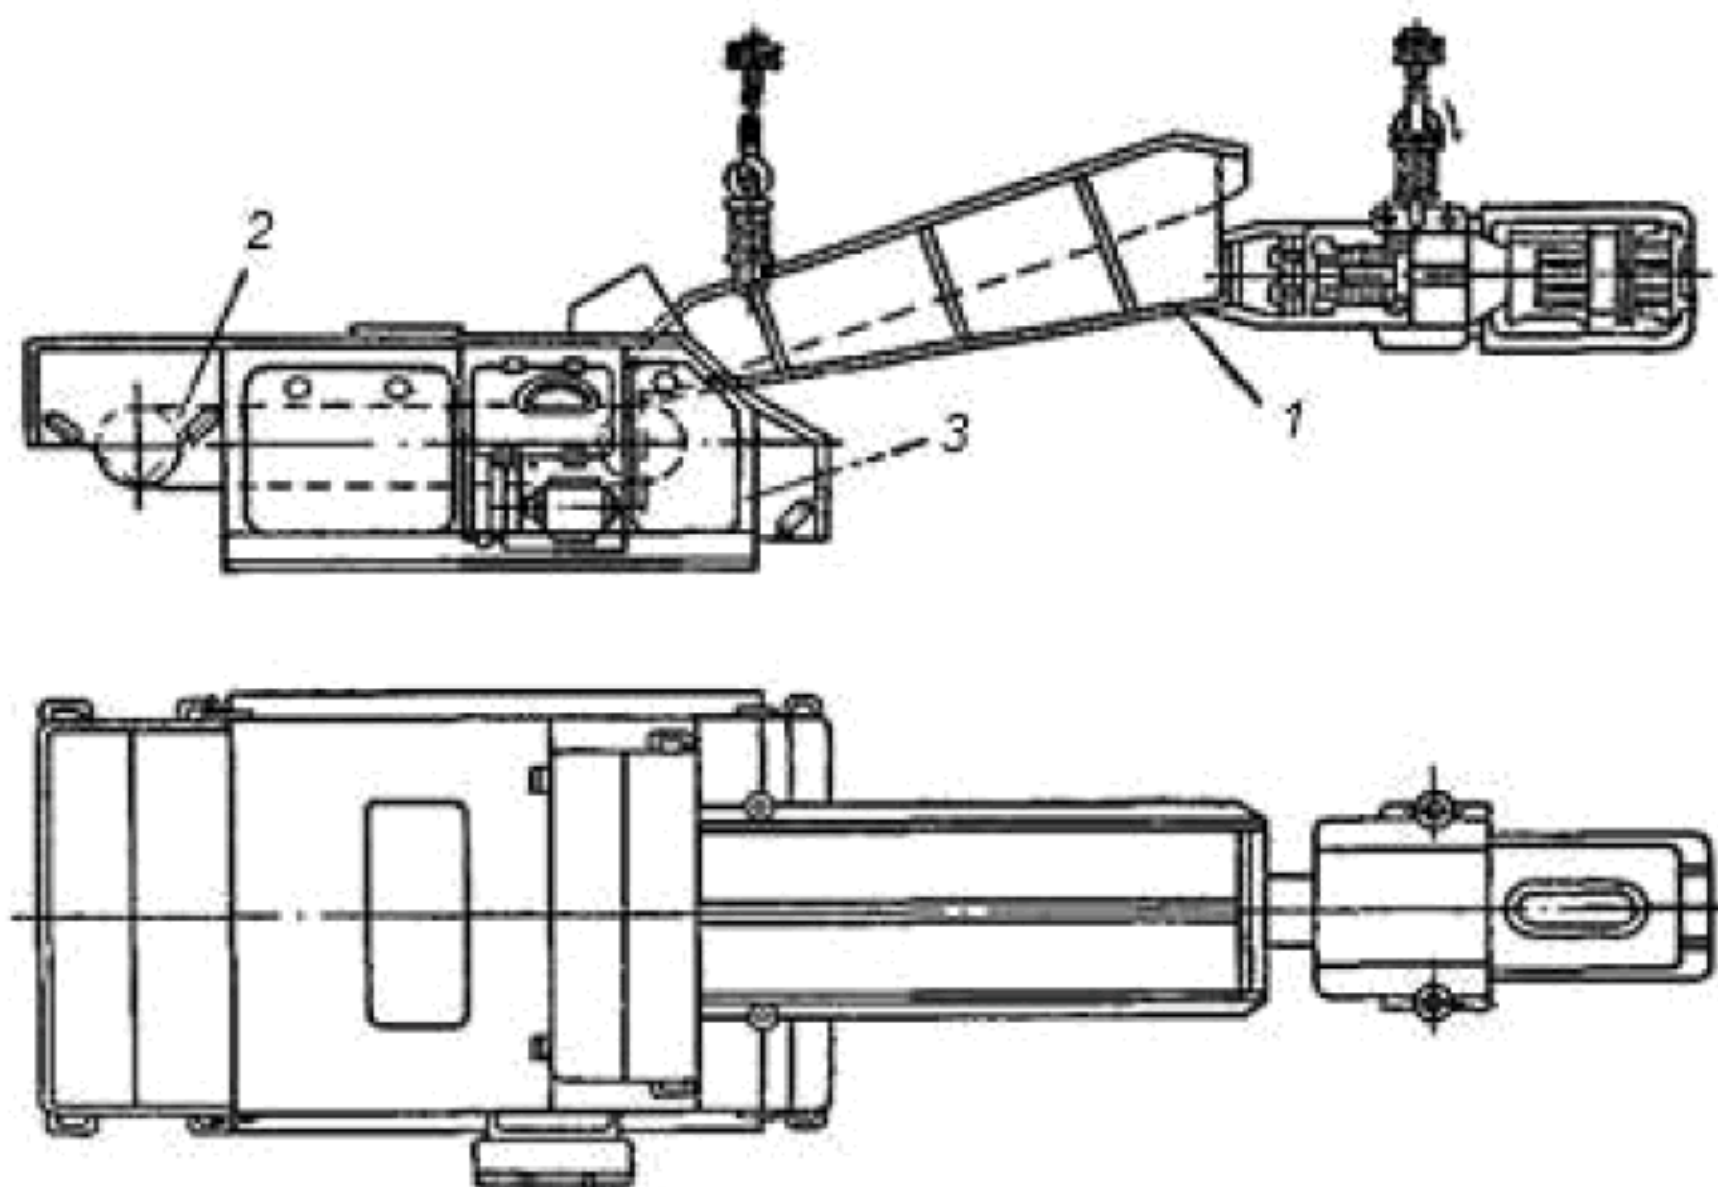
Автоматичний ваговий дозатор типу ЛДА:
